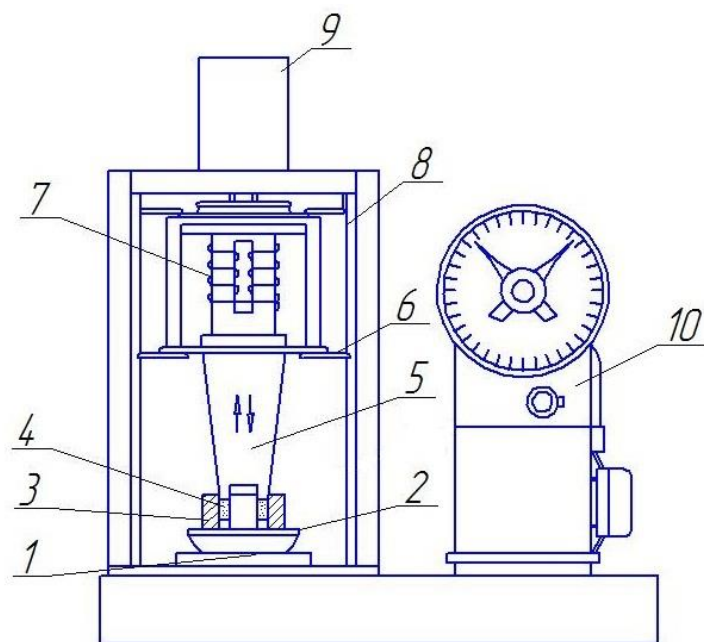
Схема установки для прессования изделий из ПКМ с наложением ультразвуковых колебаний: 1 – основание; 2 – шаровая опора; 3 – пресс-форма; 4 – порошок ПКМ; 5 – волновод-пуансон; 6 – траверса; 7 – магнитострикционный преобразователь; 8 – направляющая колонна; 9 – гидроцилиндр; 10 – гидравлическая система
